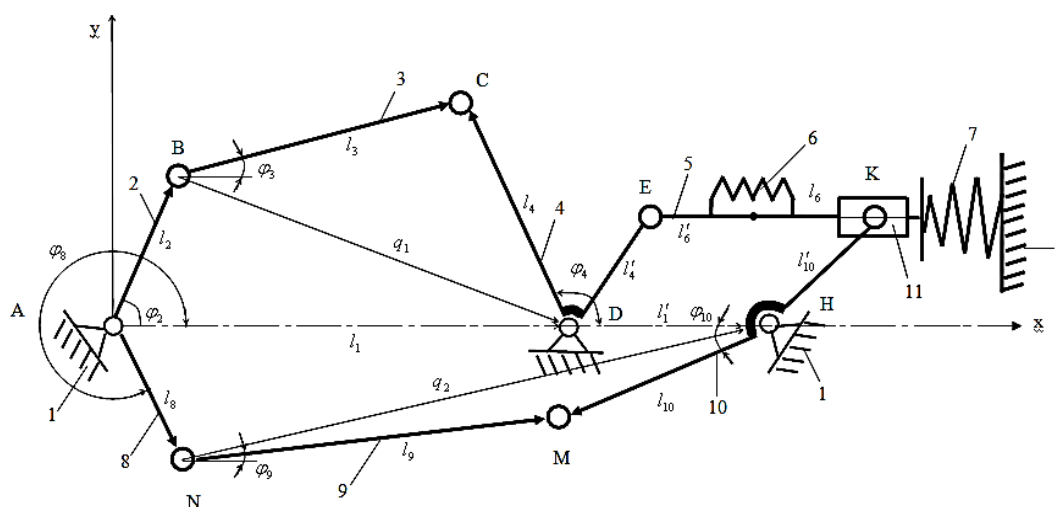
Кинематическая схема механизма перемещения материала швейной машины
